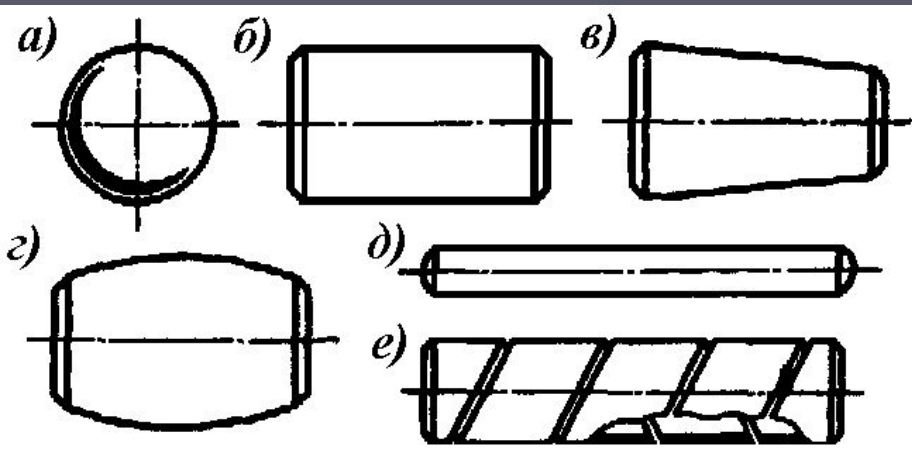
Основные формы тел качения, применяемые в подшипниках: а) шарик; ролики – б) цилиндрический; в) конический; г) бочкообразный; д) игольчатый; е) витой
